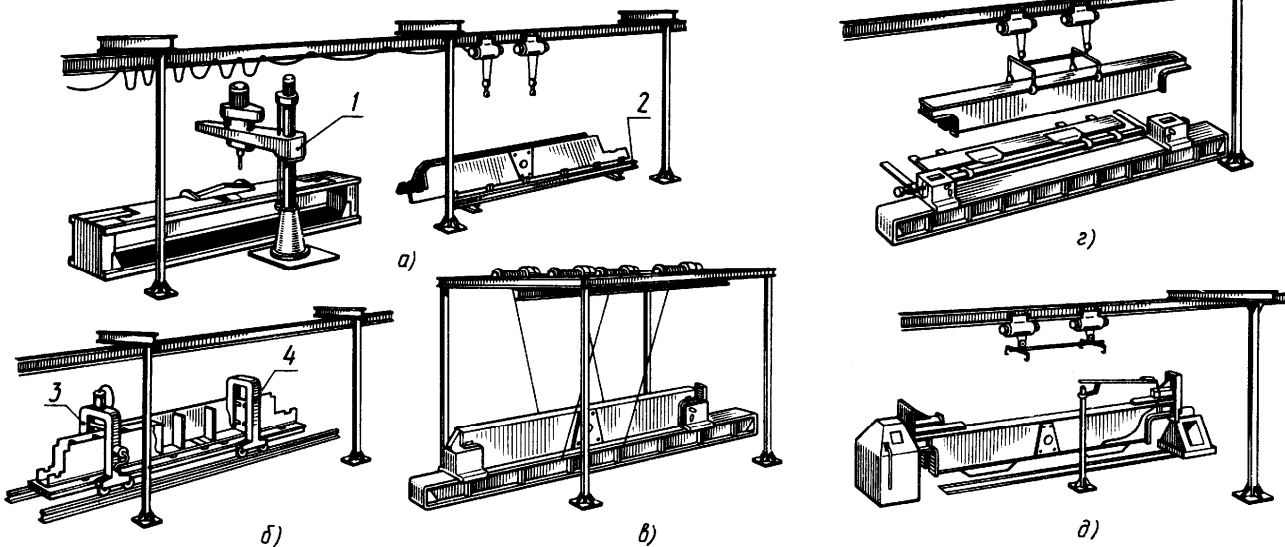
Участки поточной линии сборки и сварки концевой балки
